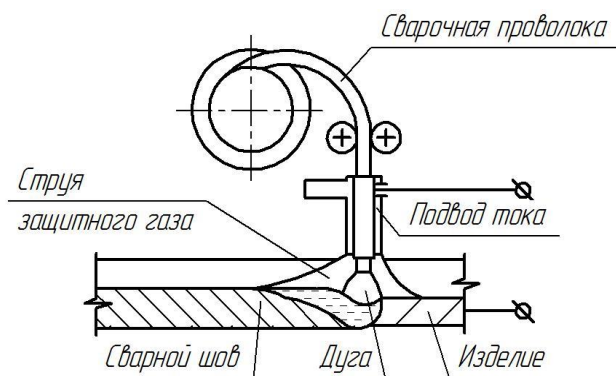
Схема механизированной сварки в защитных газах
